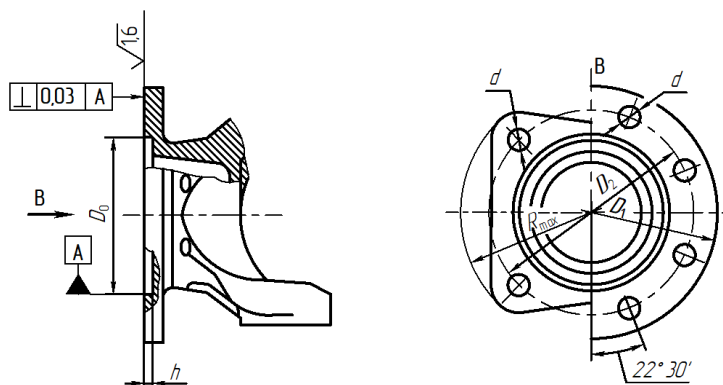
Типи фланців вилок карданних шарнірів з приєднувальними поверхнями та виточкою для центрування
